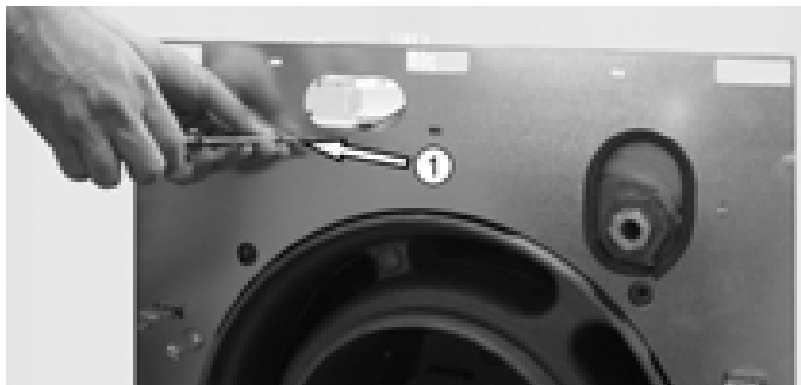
Schraube ① zur Befestigung des Reglerblechs einschrauben.
